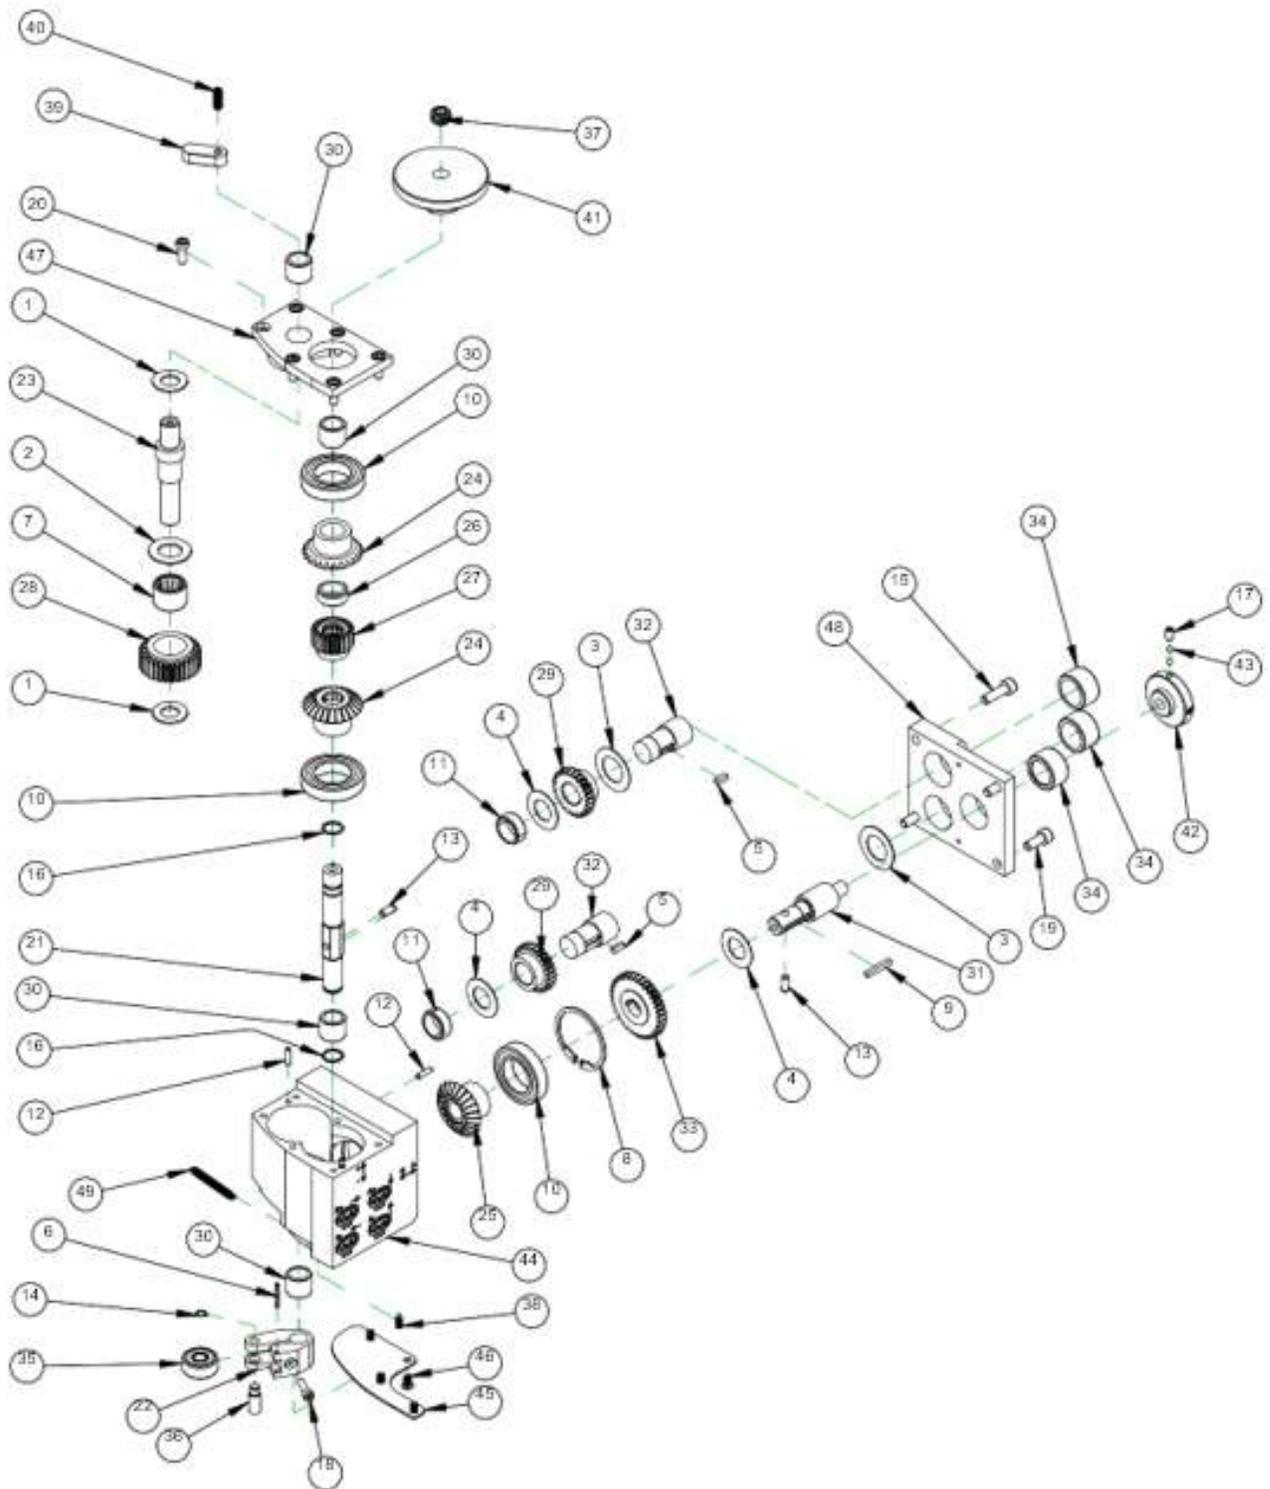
ENSEMBLE DE BOÎTIER D'AVANCE (RÉF. 79194)
